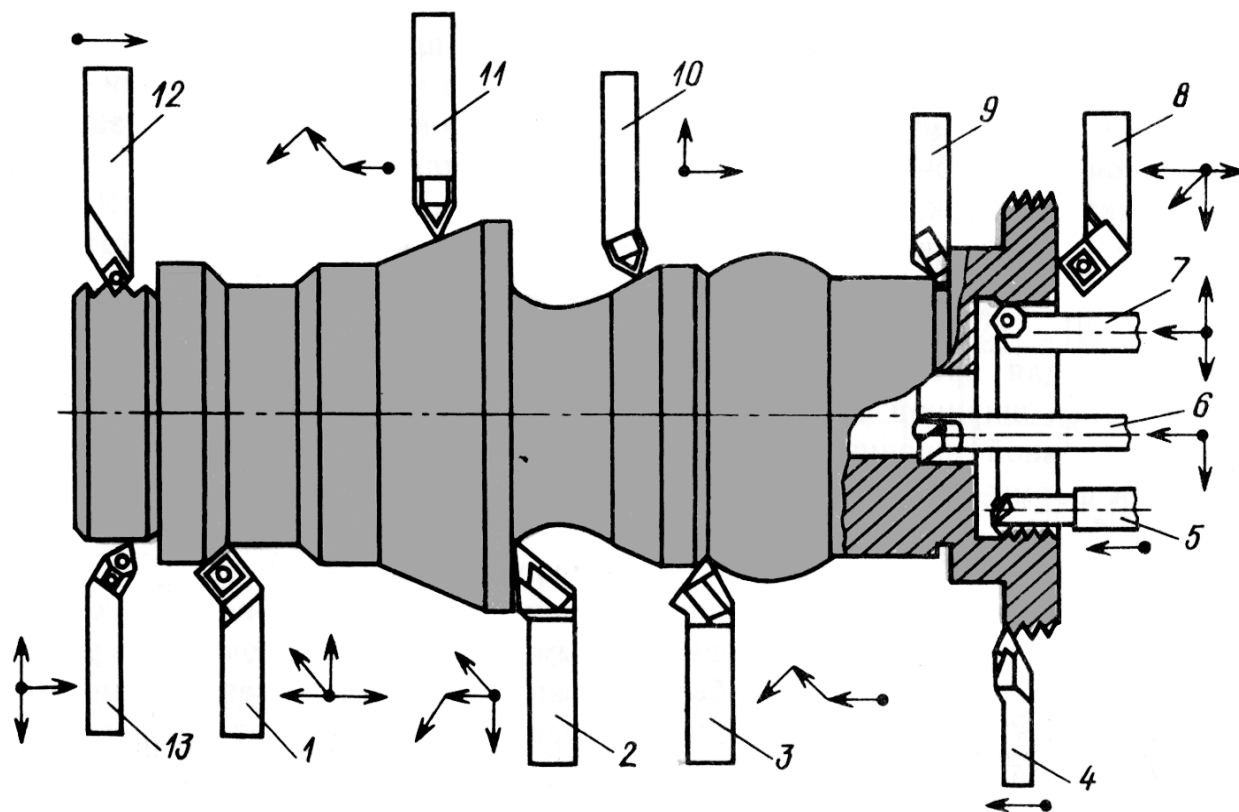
Схема обработки основных типовых поверхностей токарными резцами с МРП
